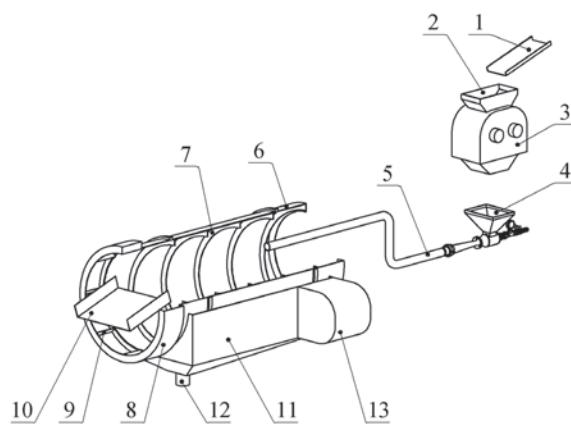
Комплекс устройств для гидромеханической разделки рыбы: 1 — гидрожелоб; 2 — приемная воронка; 3 — рыборезка; 4 — гидроэJECTор; 5 — гибкий шланг; 6 — перфорированный ротор; 7 — спираль; 8 — устройство выгрузки; 9 — лопатки; 10 — отводной лоток; 11 — поддон; 12 — выпускной патрубок; 13 — привод
